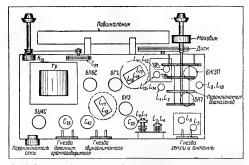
Схема расположения основных деталей на шасси приемника (вид снизу)
